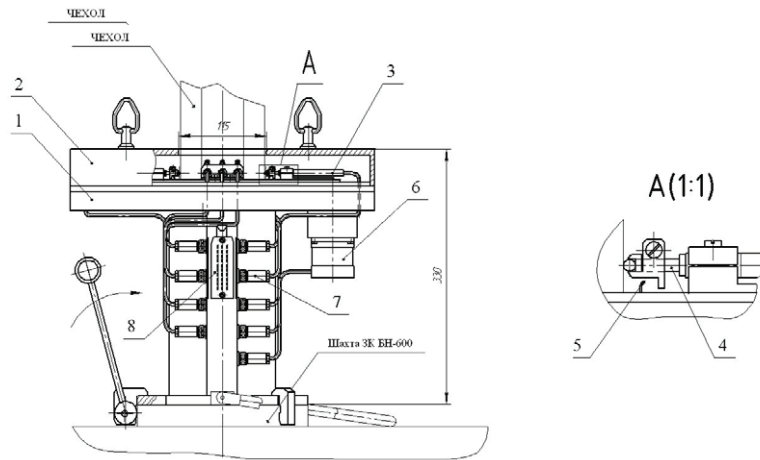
Измерительный модуль КЧС (вид сбоку): 1 – корпус; 2 – колпак защитный; 3 – первичный преобразователь; 4 – плунжер преобразователя; 5 – упругий элемент перемещения; 6 – шаговый двигатель с редуктором; 7 – соединительные кабели с разъемами; 8 – колодочный разъем подсоединения
